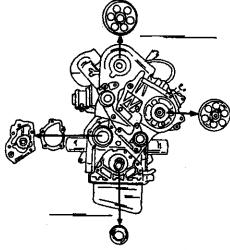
Детали, снимаемые с передней стороны двигателя.
